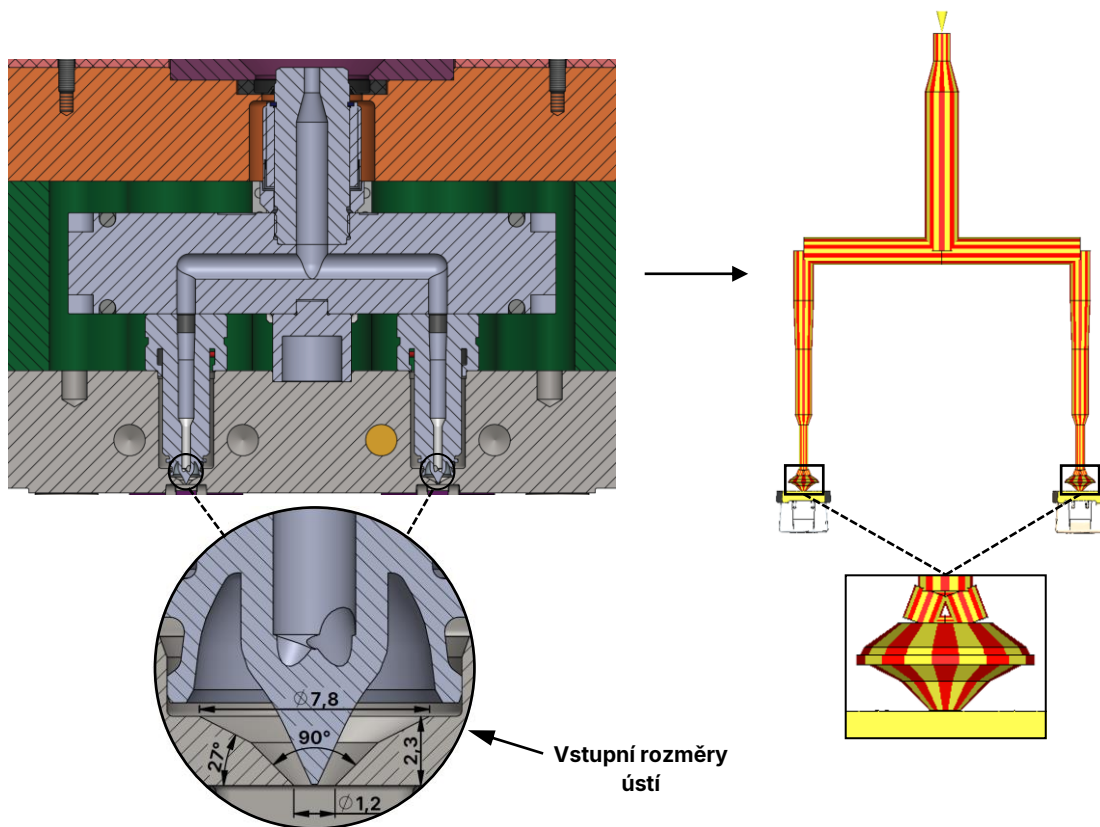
Horký vtokový systém dodávaný firmou Thermoplay S.p.A.
